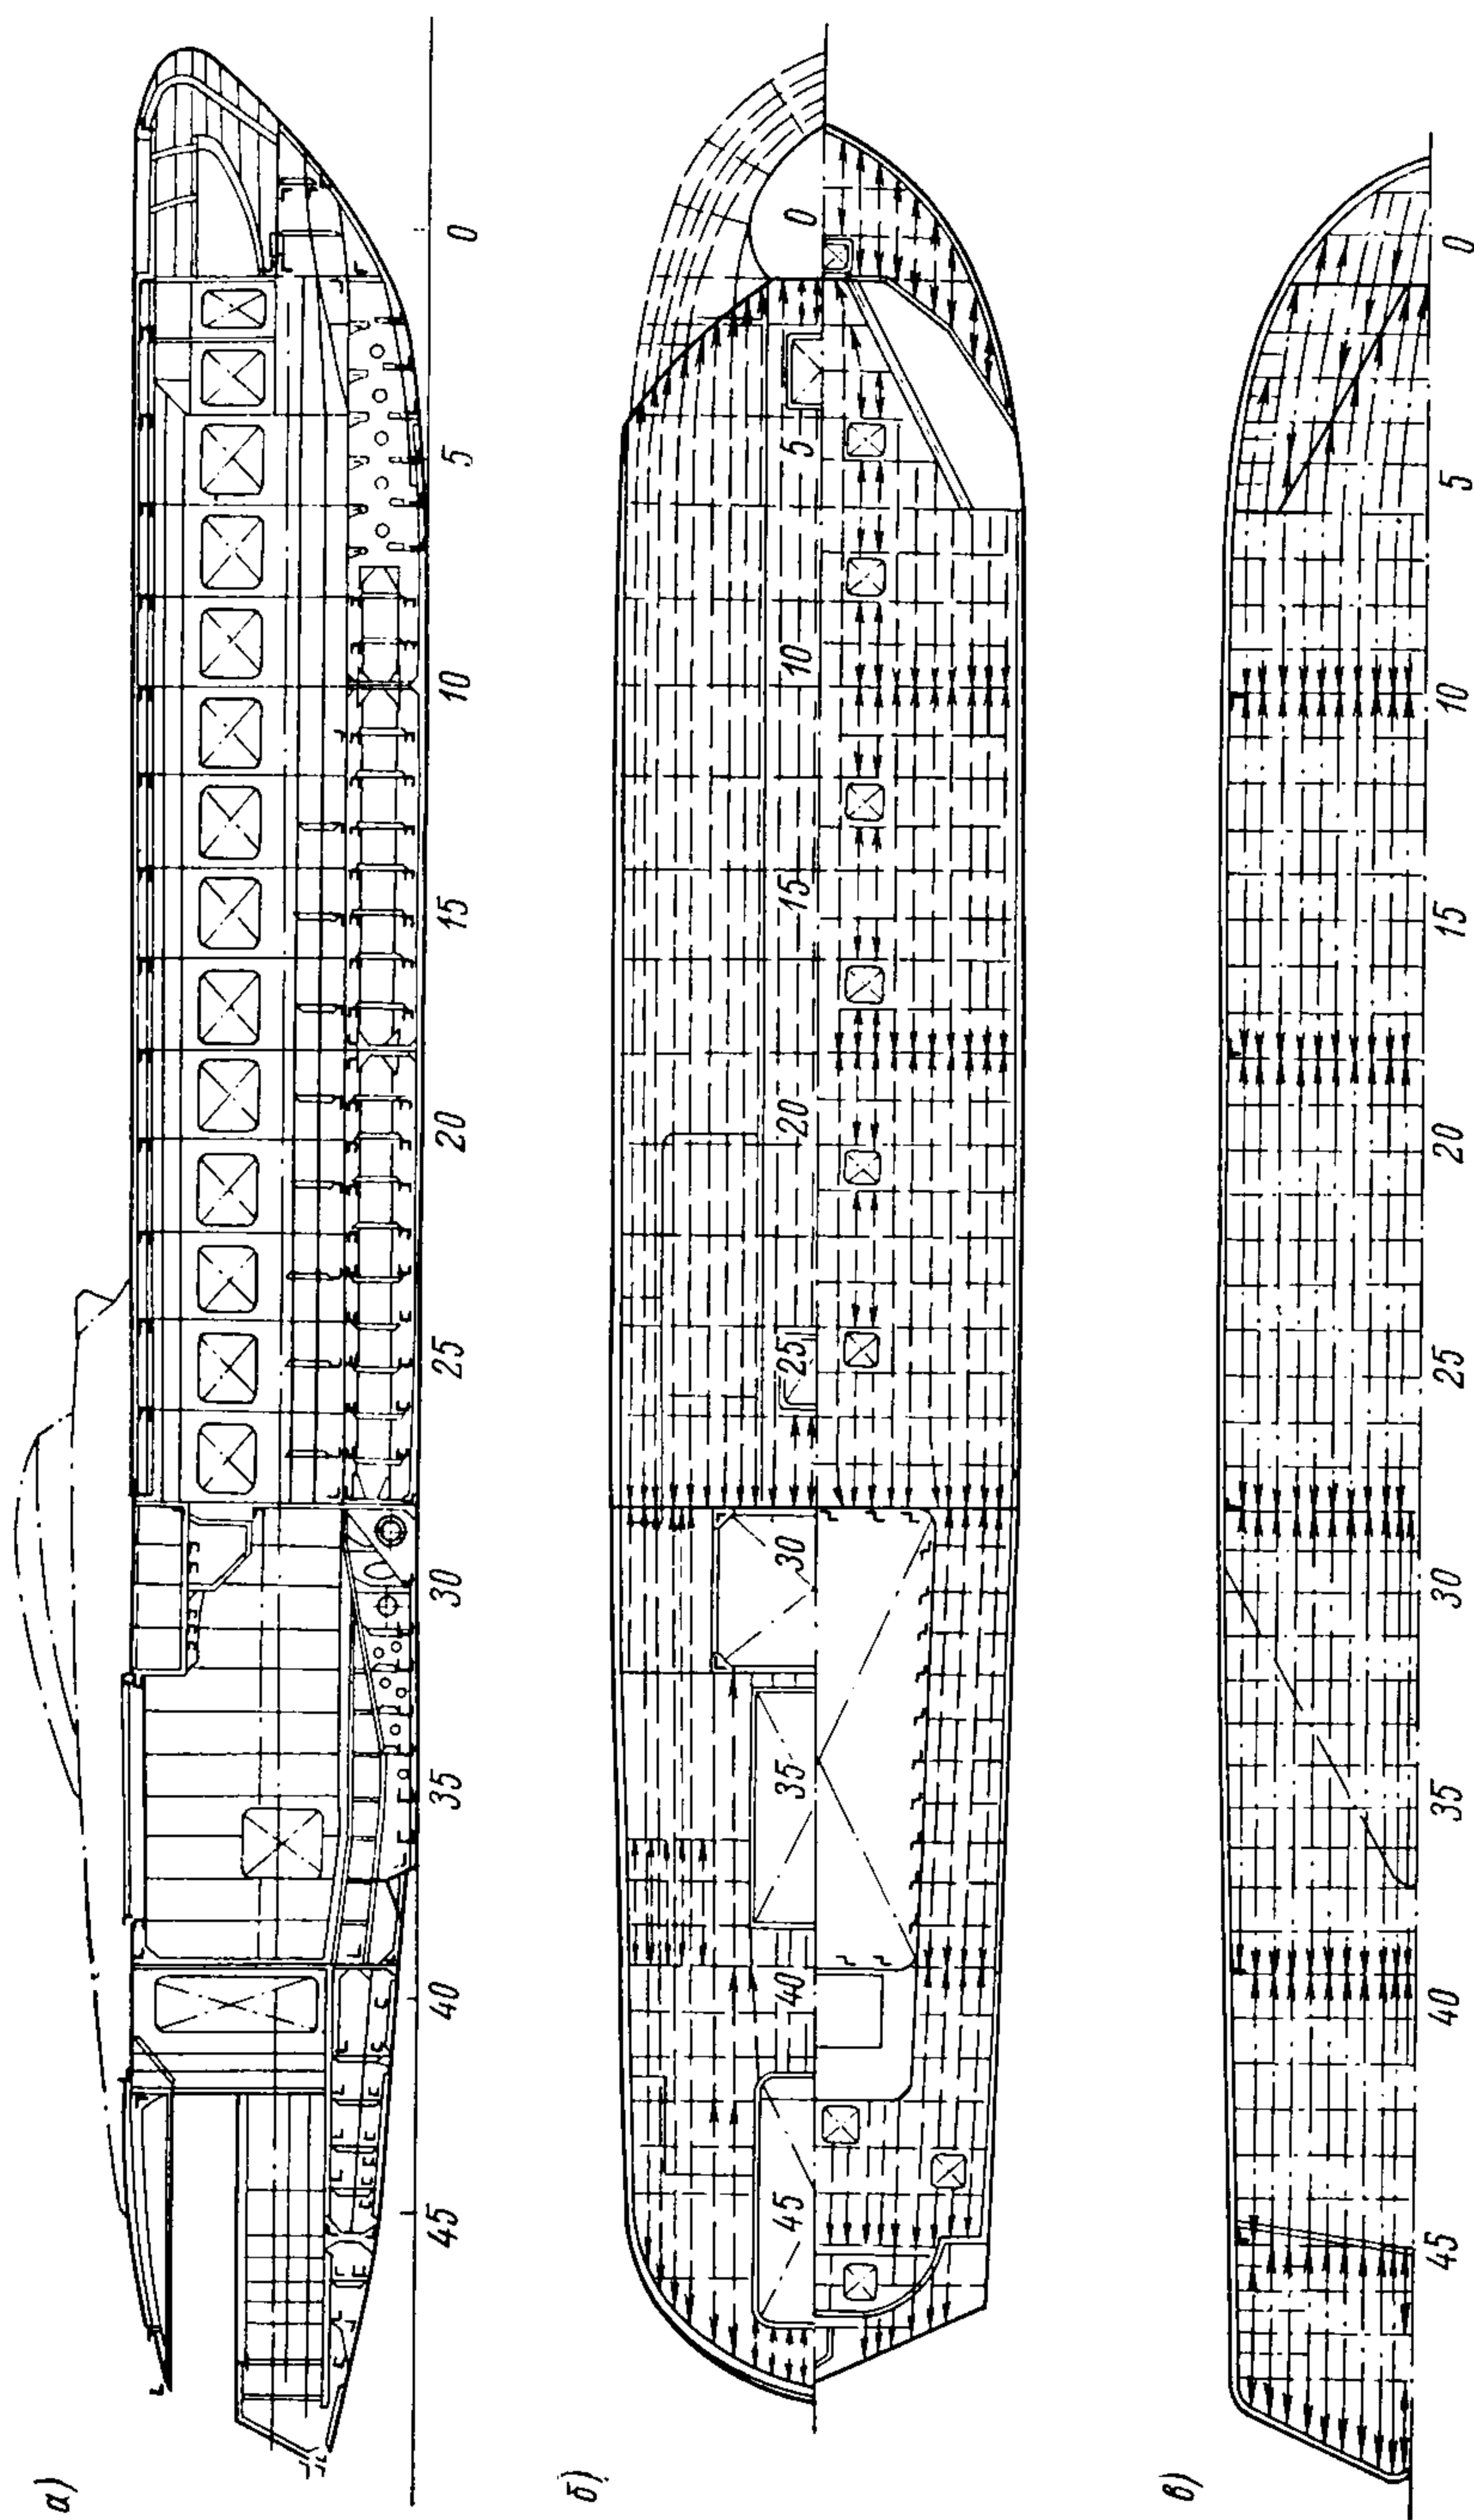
Конструктивная схема корпуса и надстройки теплохода «Ракета»: а — продольный разрез; б — план набора тентовой палубы и палубы надводного борта; в — план днищевого набора.
